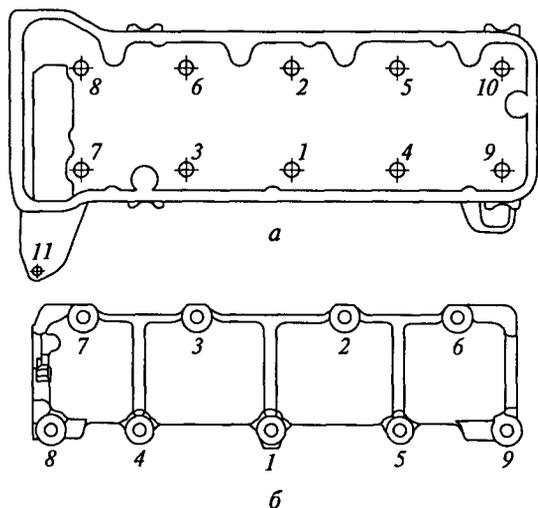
Порядок затягивания болтов головки цилиндров (а) и гаек крепления корпуса подшипников распределительного вала (б)
